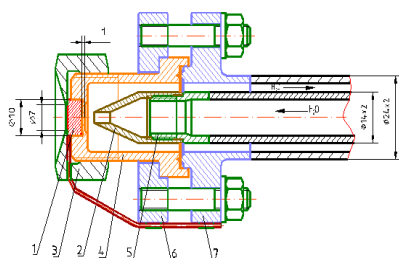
конструктивная схема устройства охлаждения облучаемого образца
